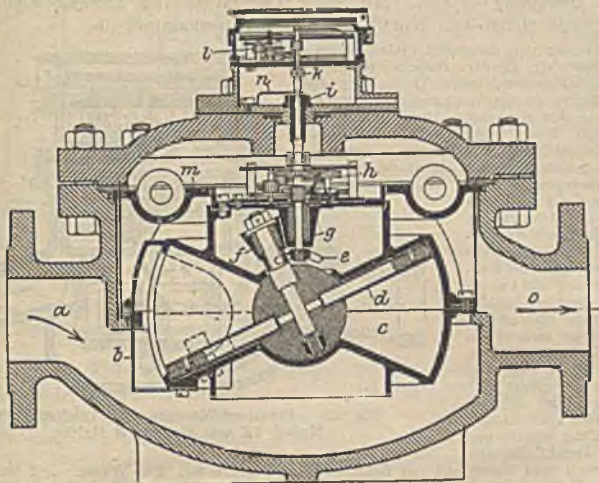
Scheibenwassermesser nach Siemens & Halske. Trockenläufer.
